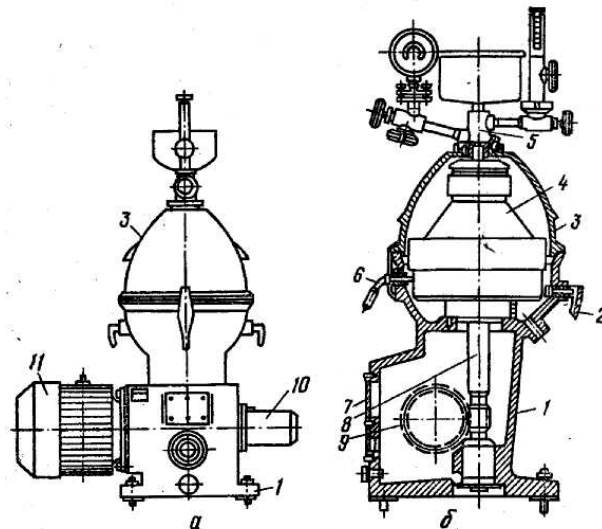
Загальний вигляд (а) і вертикальний розріз (б) сепаратора-очисника: 1 – станина; 2 – гальмо; 3 – кришка; 4 – барабан; 5 – приймально-вивідний пристрій; 6 – стопор; 7 – кришка; 8 – вал; 9 – шестерня горизонтального валу; 10 – тахометр; 11 – електродвигун.
